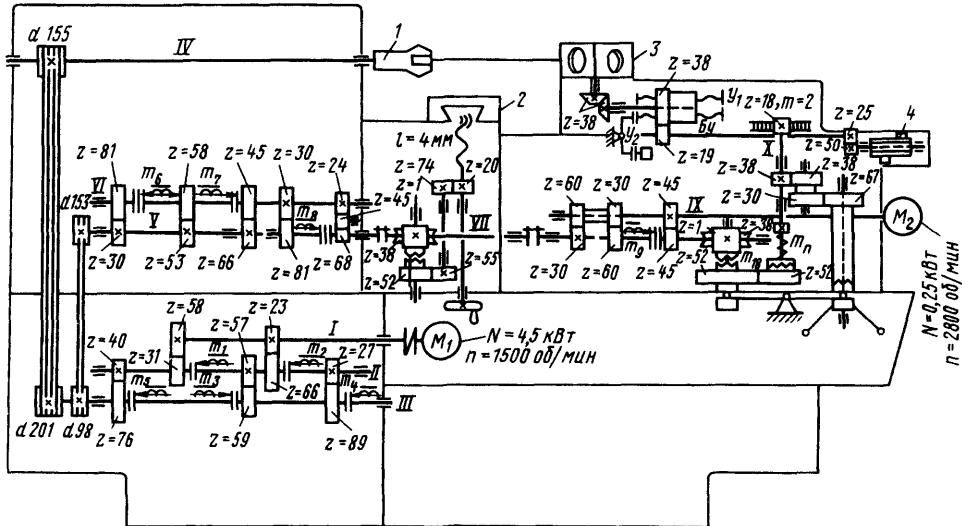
Кинематическая схема токарно-револьверного станка модели IP365
